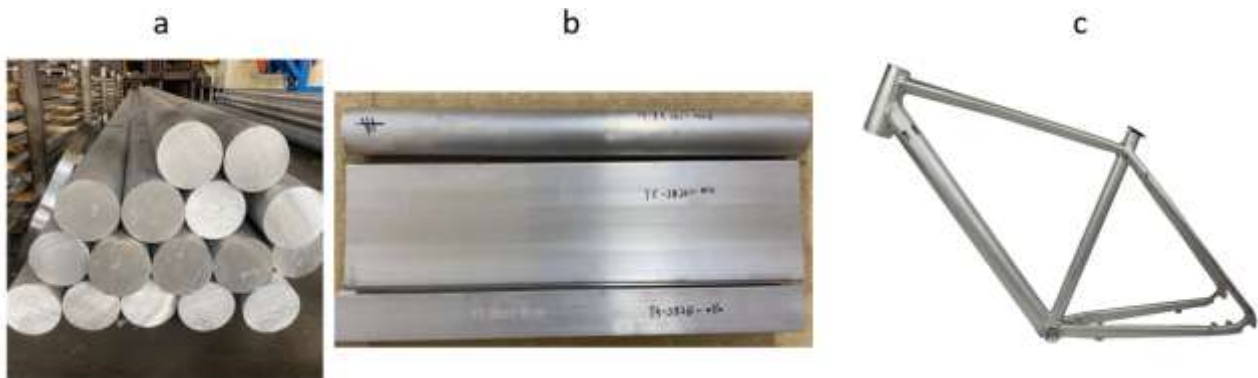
(a) billettes d'aluminium brute obtenues par coulée. (b) différentes géométries de profils obtenues par extrusion des billettes. (c) exemple d'un cadre de vélo après soudage.
